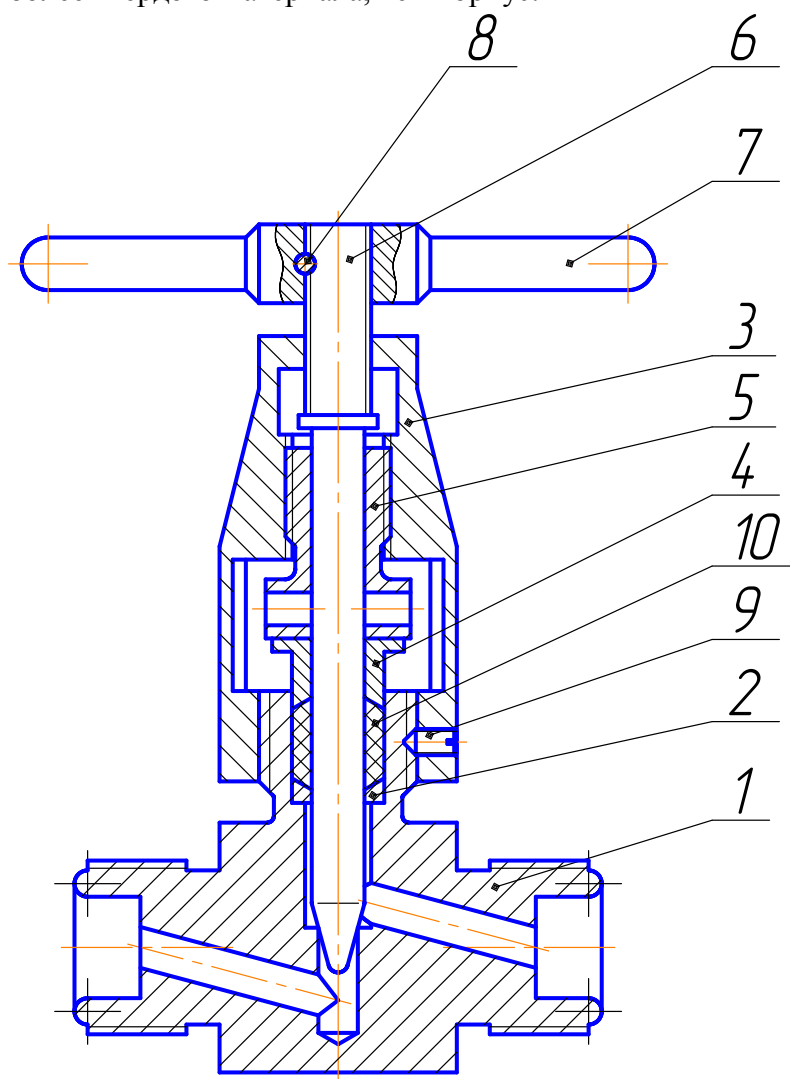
Клапан игольчатый, проходной, регулирующий
